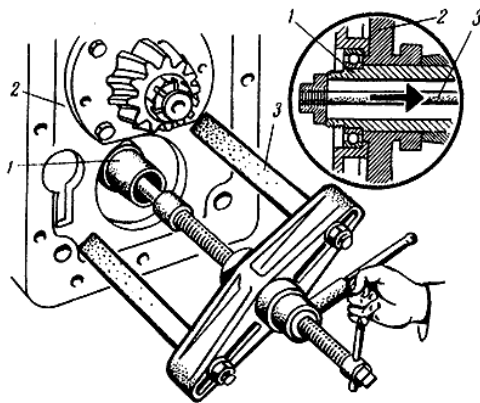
Выпрессовка промежуточного вала: 1 — промежуточный вал; 2 — корпус КПП; 3 — съемник
